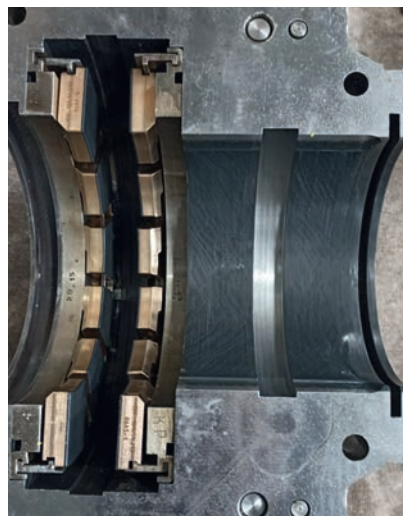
Опорно-упорный подшипник ротора осевого компрессора турбины высокого давления после 3016 ч эксплуатации
